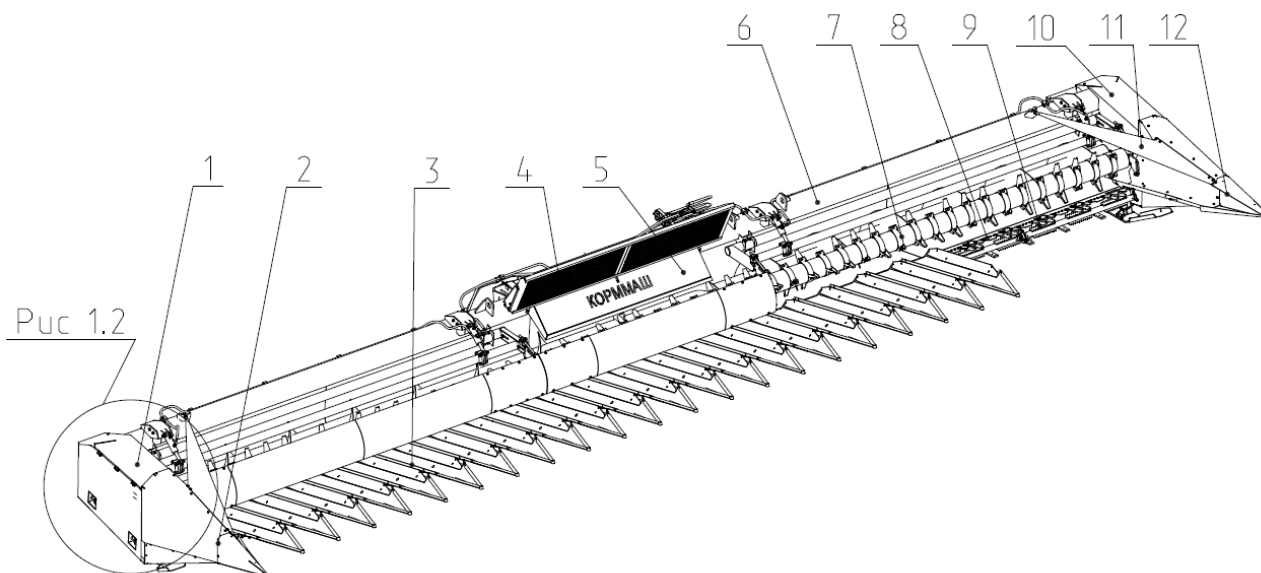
Общий вид жатки ЖНС-9,5 ПГ
